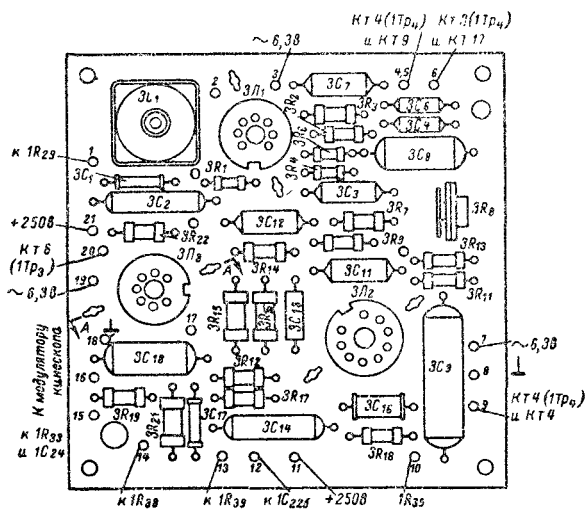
Расположение деталей на печатной плате задающего генератора и АПЧФ строчной развертки телевизоров «Рубин-110» и «Рубин-111».
